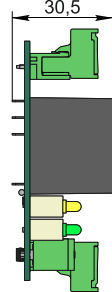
Габаритные размеры модулей ЭНИ-760-32к-ПК-01
